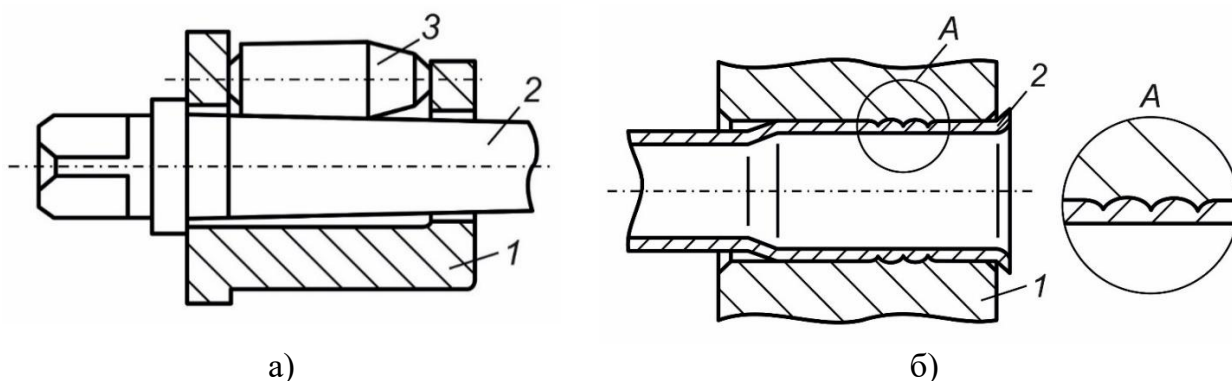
а) принципиальная схема роликовой вальцовки: 1 – корпус, 2 – конус, 3 – вальцовочные ролики; б) схема завальцовки трубы в трубной решетке: 1 – трубная решетка, 2 – труба
